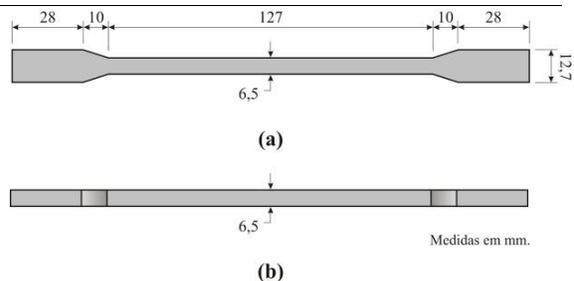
Dimensões dos corpos de prova. Vista em planta (a) e lateral (b).
